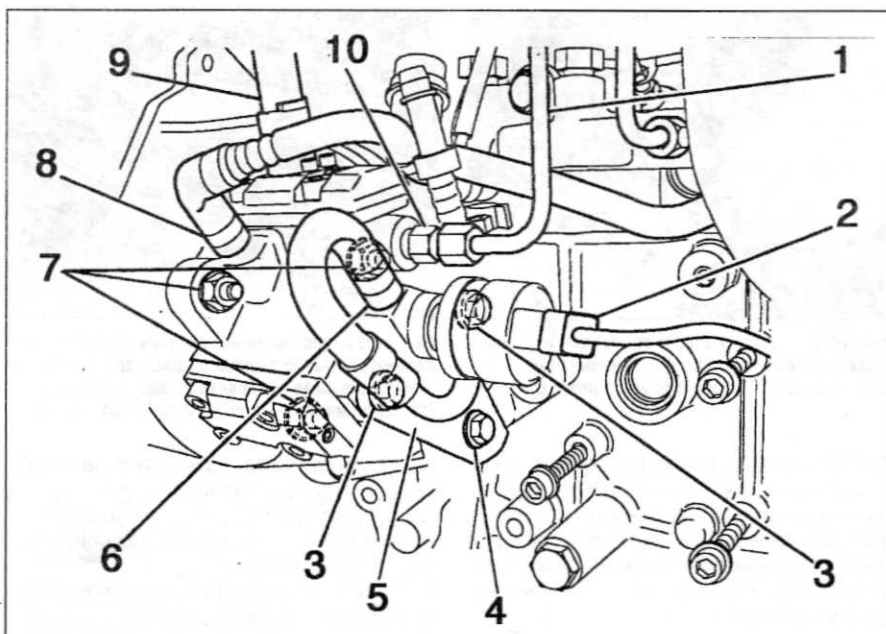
Топливный насос высокого давления (модели с двигателем 2.0 л)
